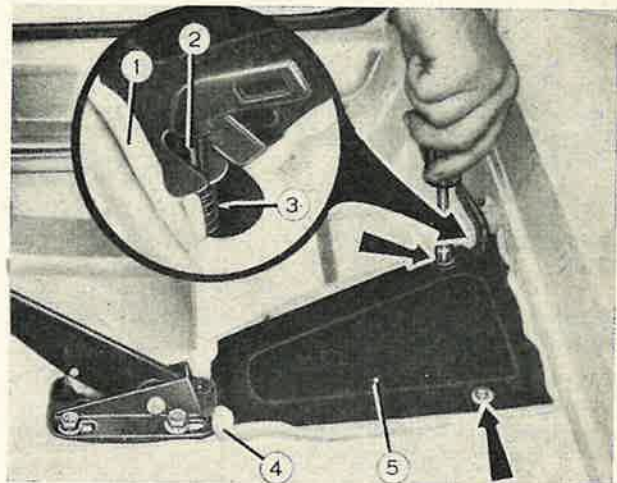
Dépose du couvercle arrière de convoyeur d'air chaud.
